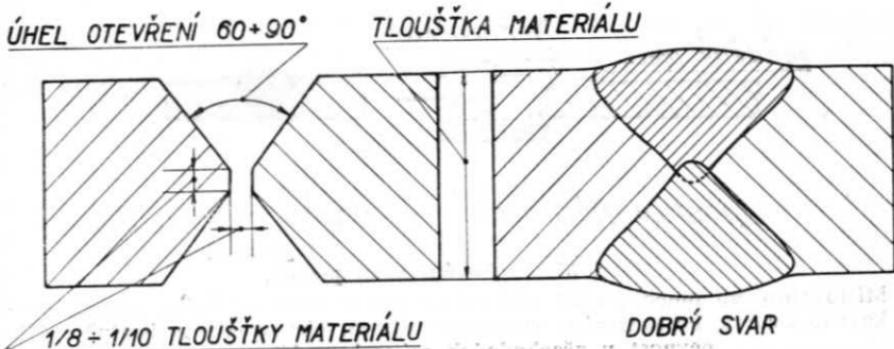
Sváření ve tvaru V u tlouštěk materiálu od 5 do 10 mm.
